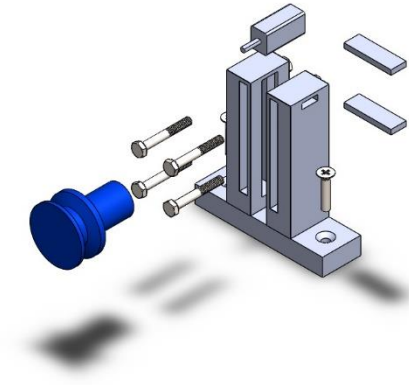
Vista explosionada motor secundario. Fuente: Propia.
